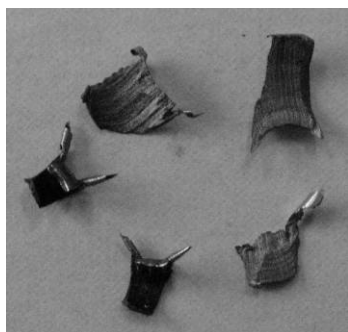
Найбільш характерні форми стружки при зубофрезеруванні стандартною фрезою та фрезою запропонованої конструкції
